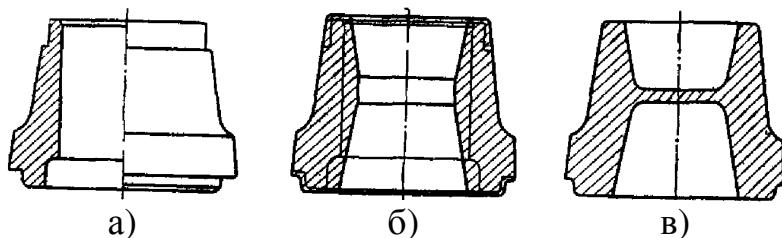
Креслення деталі (а) і штампованої заготовки для неї (б, в)
